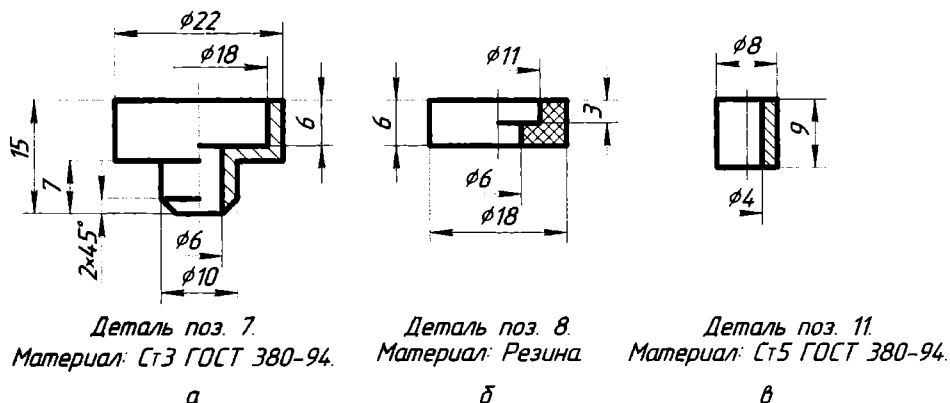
Чертежи: а — клапана; б — вкладыша; в — трубки
